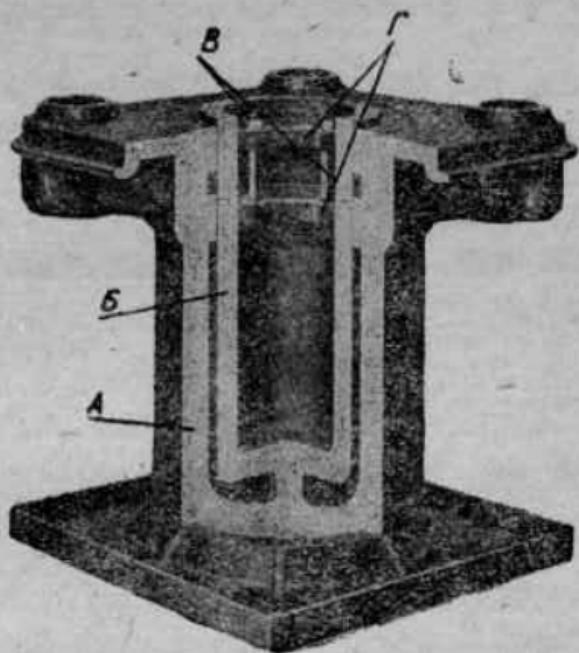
Цилиндр и пистон полуоткрытого пресса.
